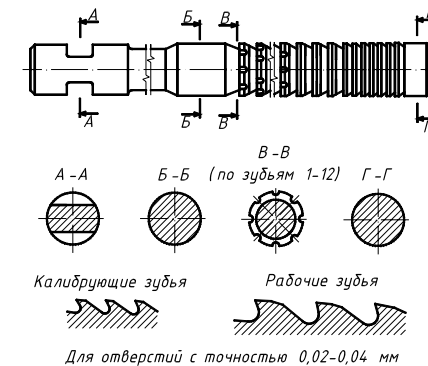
Конструкция эвольвентной шлицевой протяжки для шлицевых отверстий с эвольвентным профилем боковых сторон шлица
